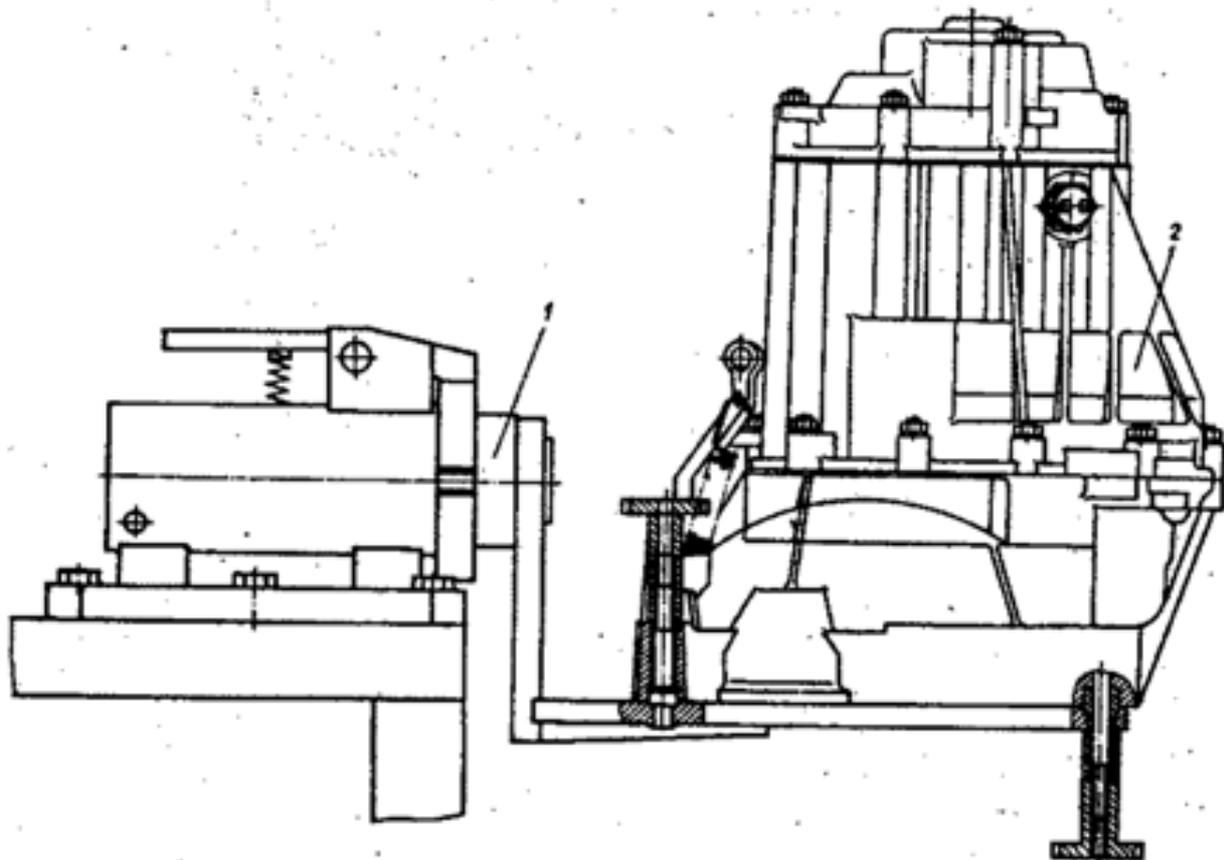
Коробка передач, установленная на приспособлении для разборки и сборки: 1 - приспособление М9832-354; 2 - коробка передач; 3 - выключатель заднего хода
